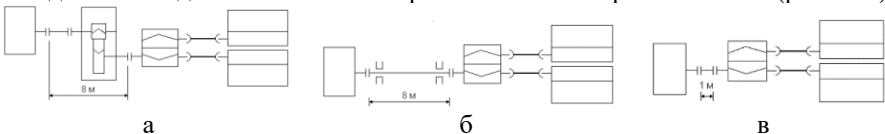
Схема лінії приводу прокатних клітей чистової групи: а) існуюча схема з редуктором, б) заміна редуктора довгим проміжним валом, в) встановлення електродвигуна безпосередньо на місце редуктора.
